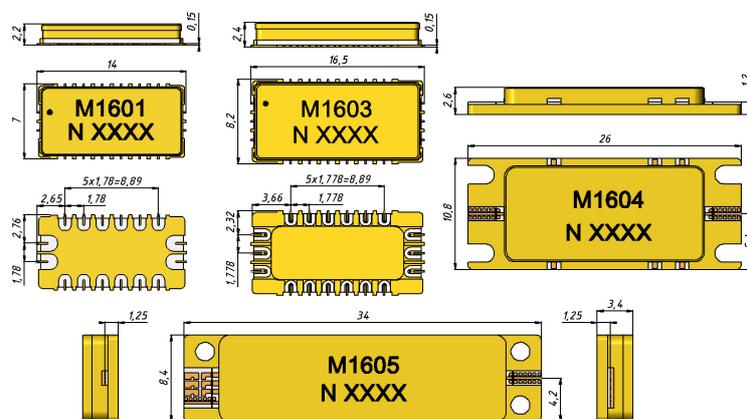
Габаритные и присоединительные размеры разработанных микрокорпусов
